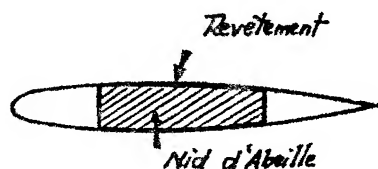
STRUCTURE SANDWICH (CAISSON DU TRIDENT)
